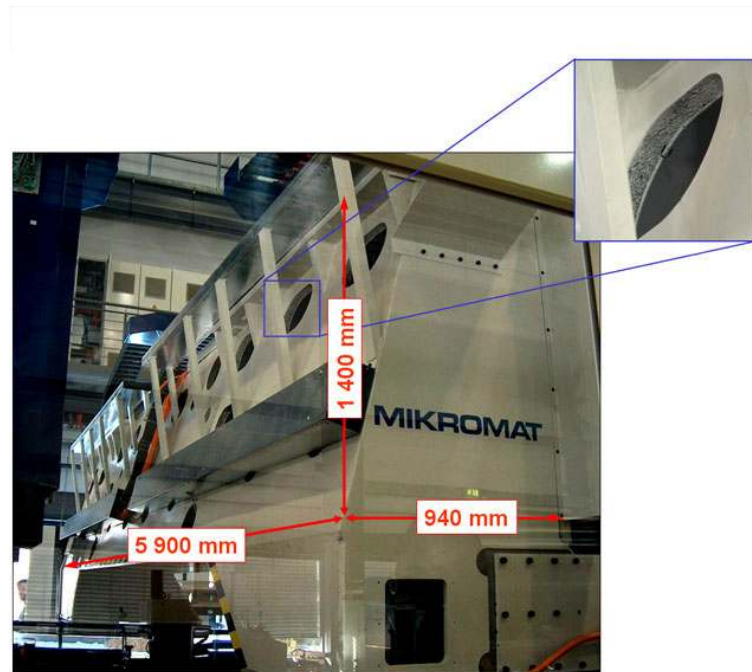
Struttura per centro di lavoro per lavorazione di utensili di grandi dimensioni [Neu03]
